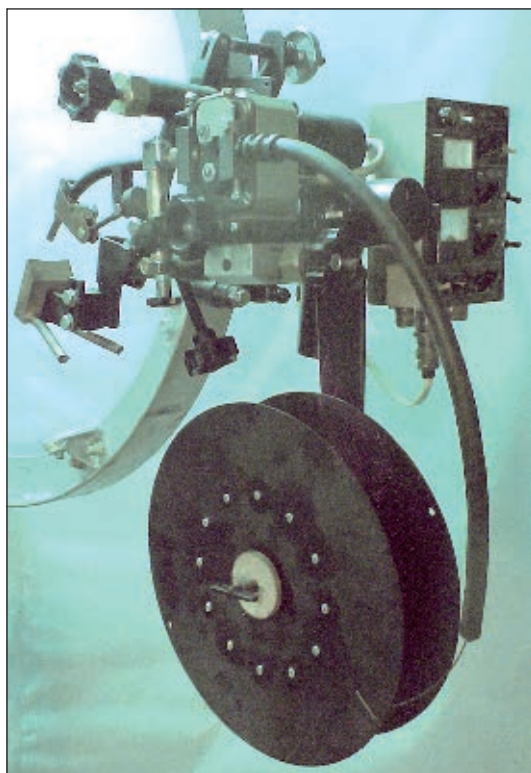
Самоходная сварочная правая головка автомата АД 365Т для сварки неповоротных стыков труб
